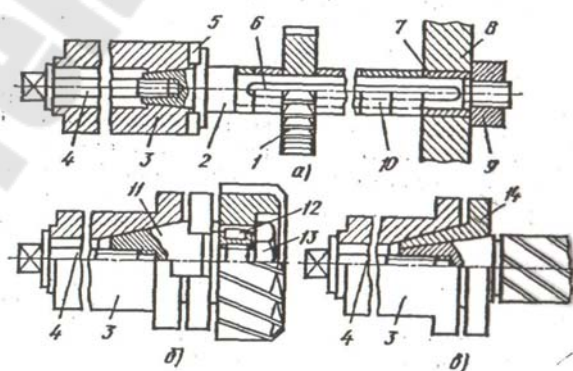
Схемы крепления инструмента на фрезерных станках
